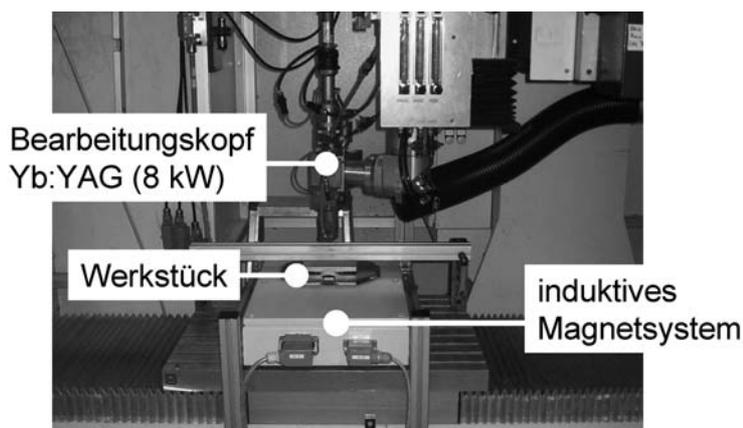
Induktives Magnetsystem integriert in eine Laserschweißanlage. Das Magnetsystem befindet sich unterhalb des Werkstücks. Der Bearbeitungskopf zum Schweißen mit 1- μ m-Strahlung musste nicht modifiziert werden.
